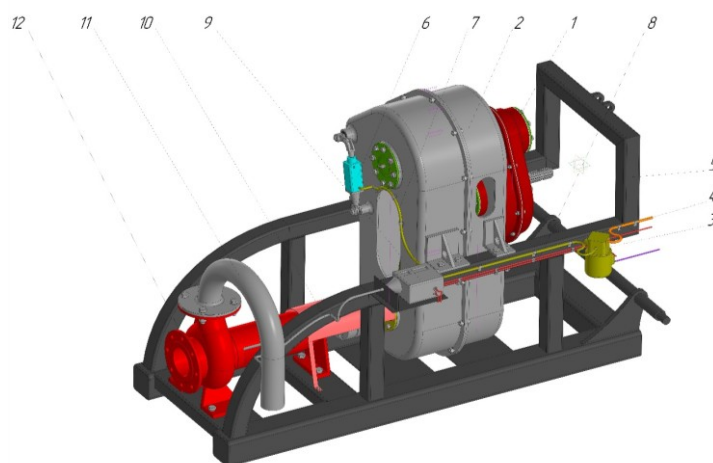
Адаптированная насосная станция: 1 – повышающий редуктор; 2 – клиноременный вариатор; 3 – электропневматический клапан; 4 – воздушная магистраль приема воздуха; 5 – рама; 6 – пневмоцилиндр с фронтальной пружиной; 7 – воздушная магистраль подачи воздуха; 8 – плюсовой кабель; 9 – реле давления; 10 – капиллярная трубка; 11 – труба подачи; 12 – насосная станция.
